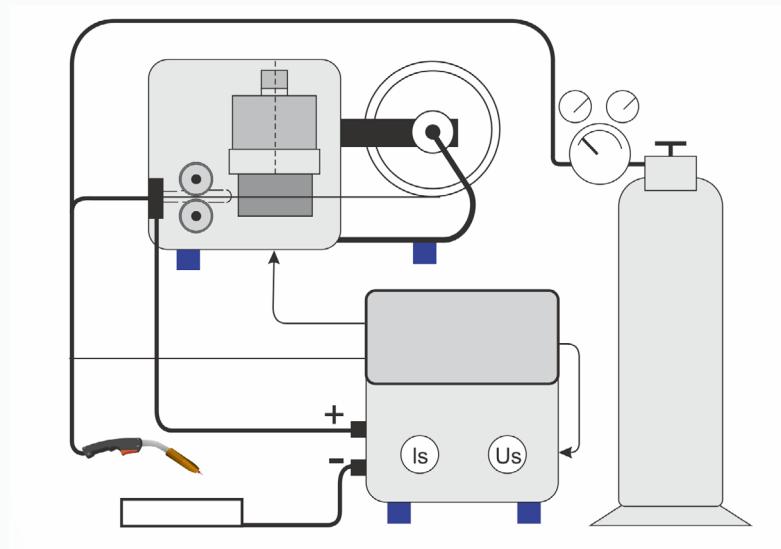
Identificación de los componentes del equipo de soldadura GMAW
